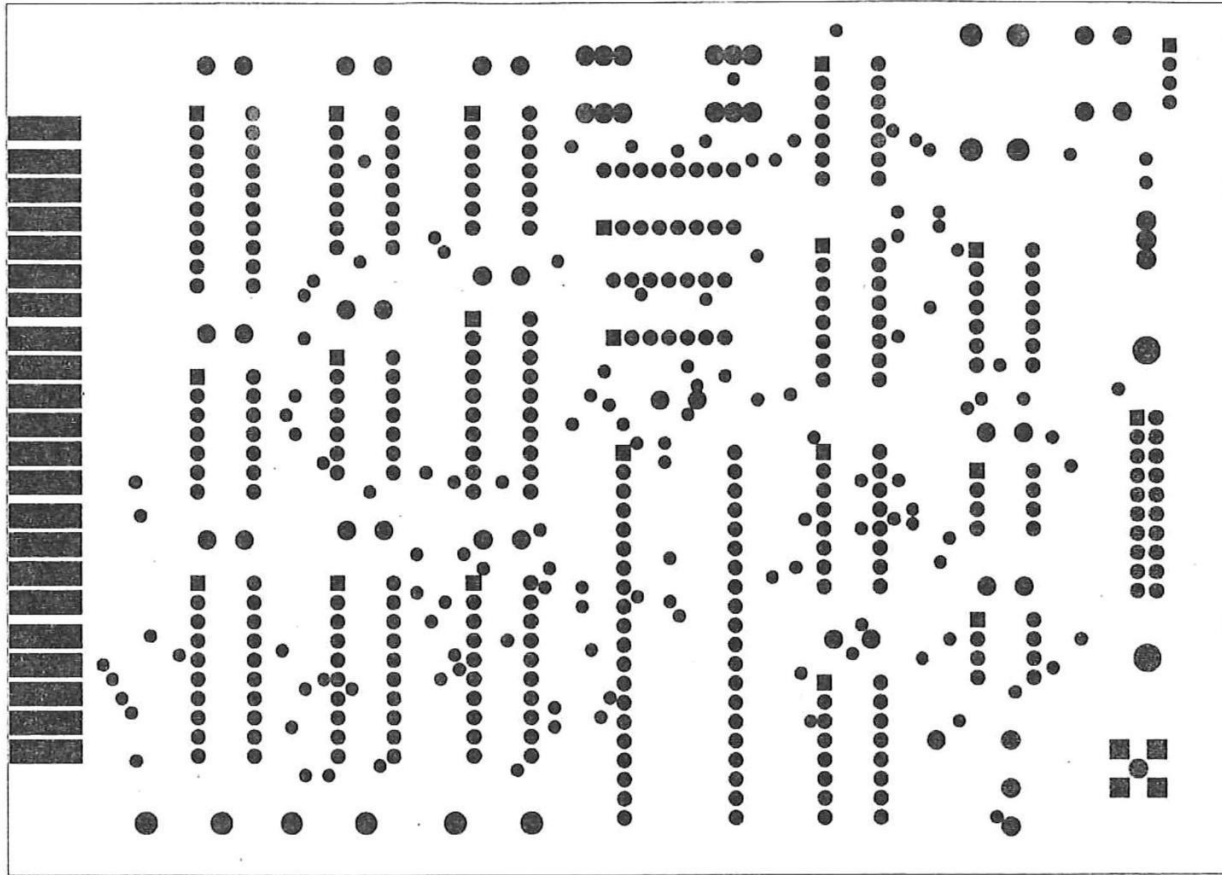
Mascarilla de soldadura de la tarjeta de control y adquisición de datos.
